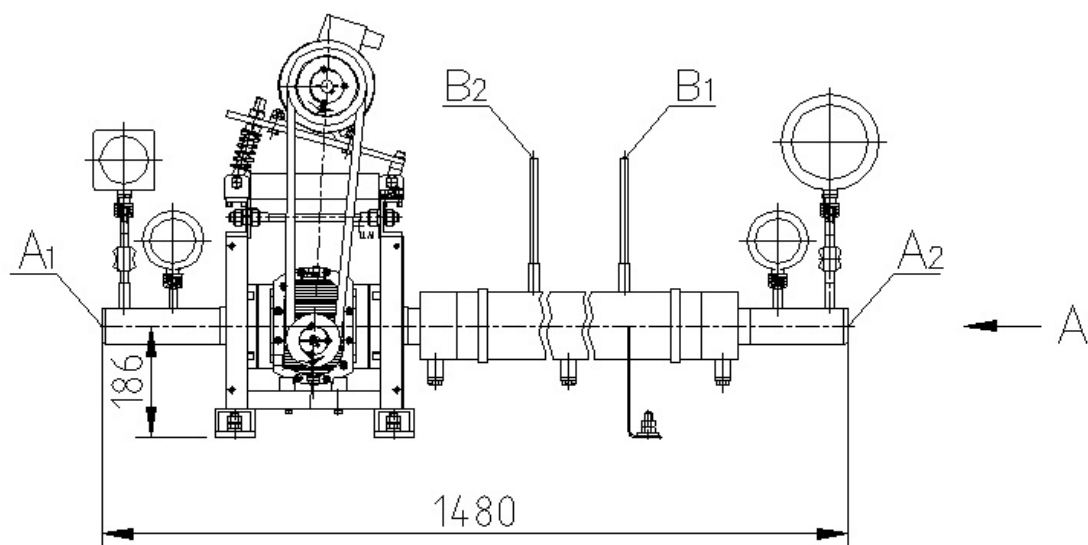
Габаритный чертеж газодувки KUK50AN001,
